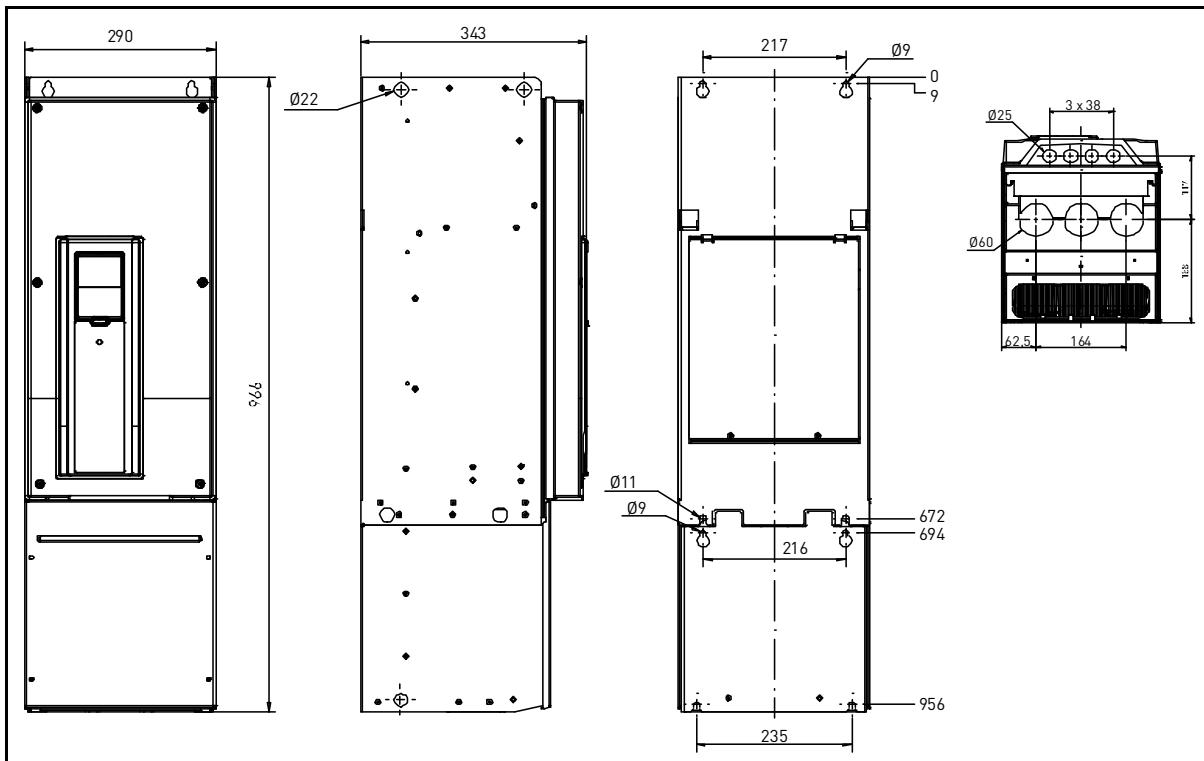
Dimensões do inversor de CA Vacon, MR8 IP21 e IP54
